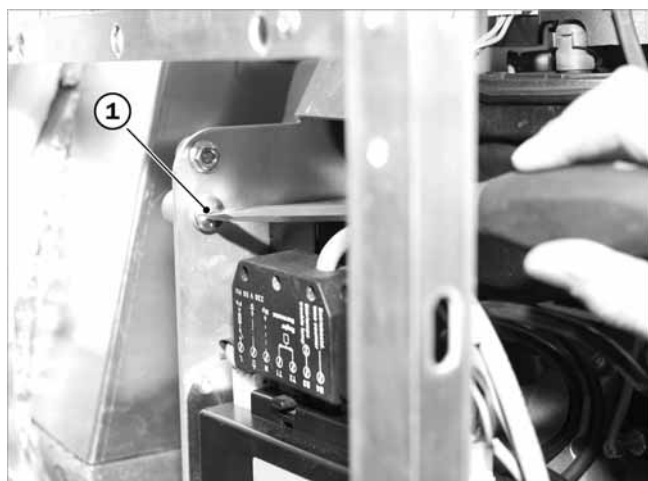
Schnellverschlusschrauben an Brenneinsatz
